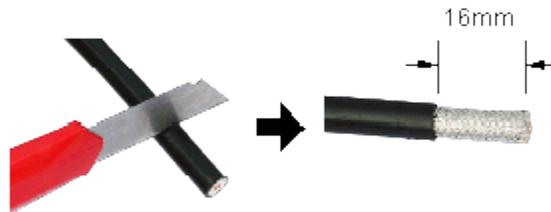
Retirar la cubierta del cable y la capa aislante. Extraído de [11]
